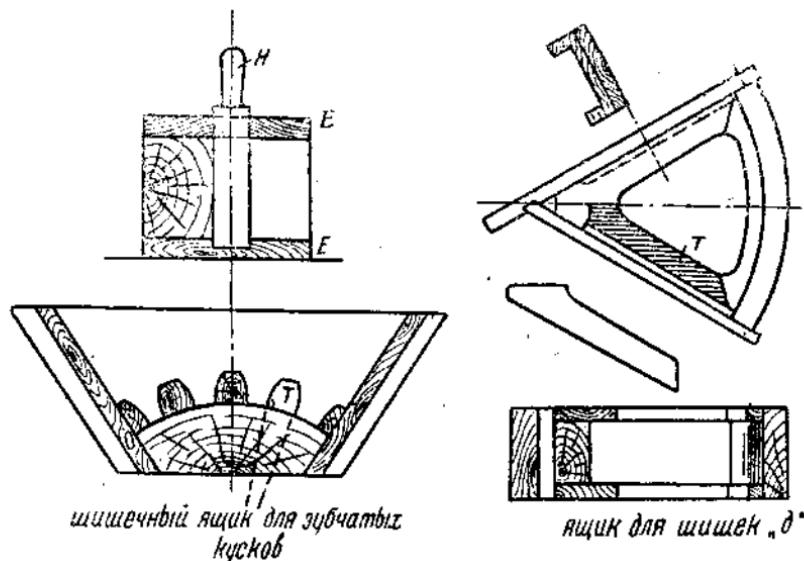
а. Шишечные ящики для шаблонной формовки зубчатого колеса.
